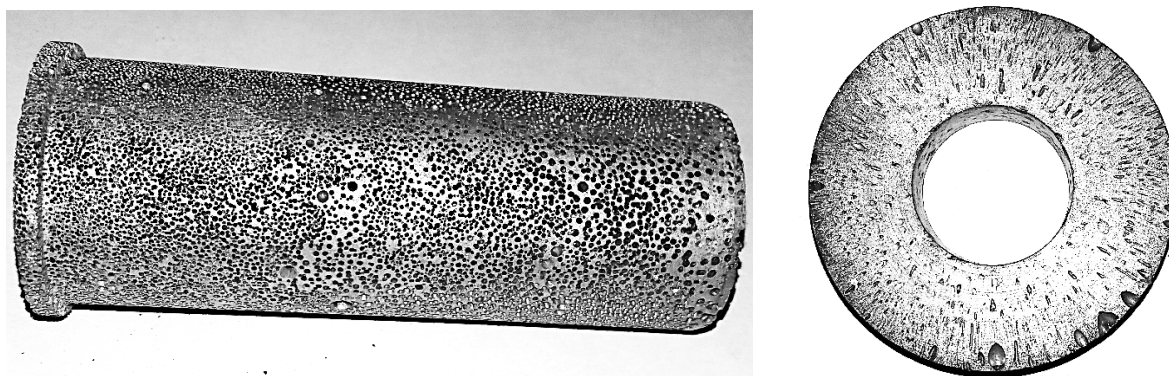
Вид заготовок подшипника скольжения со стенкой разной толщины из бронзы БрА9
